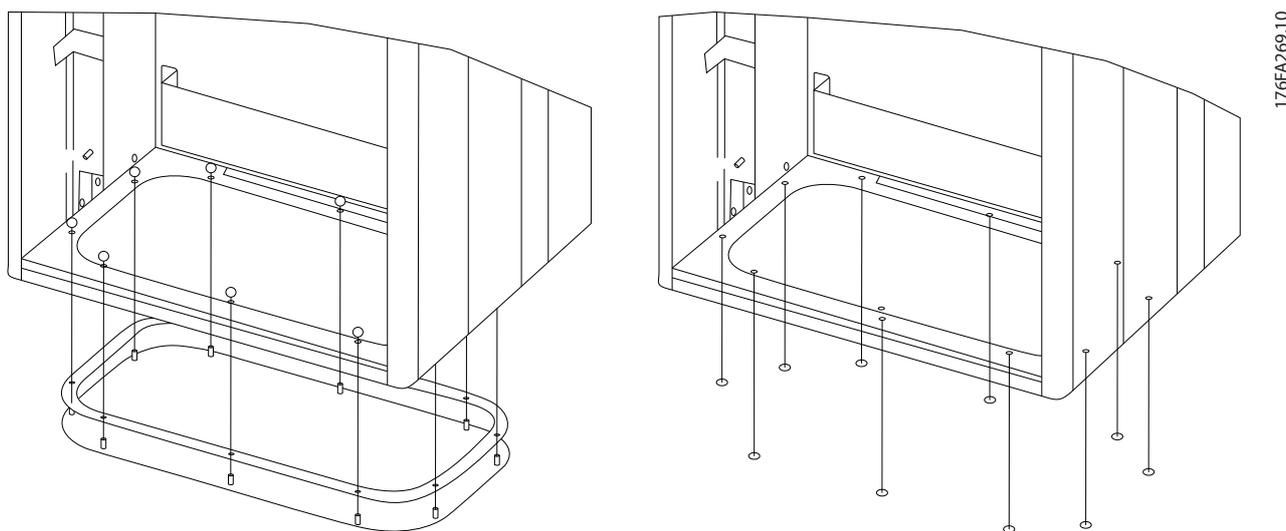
Montagem da placa inferior, Chassi de Tamanho E1.
